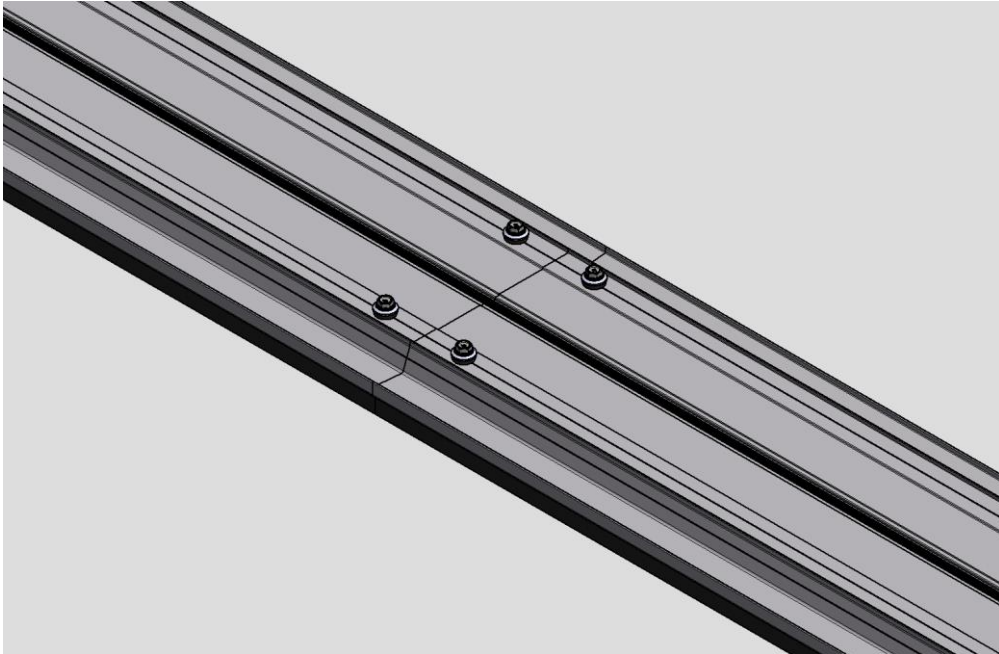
Bodenschienen zusammenfügen und mit 2 weiteren Dünnschrauben verschrauben
